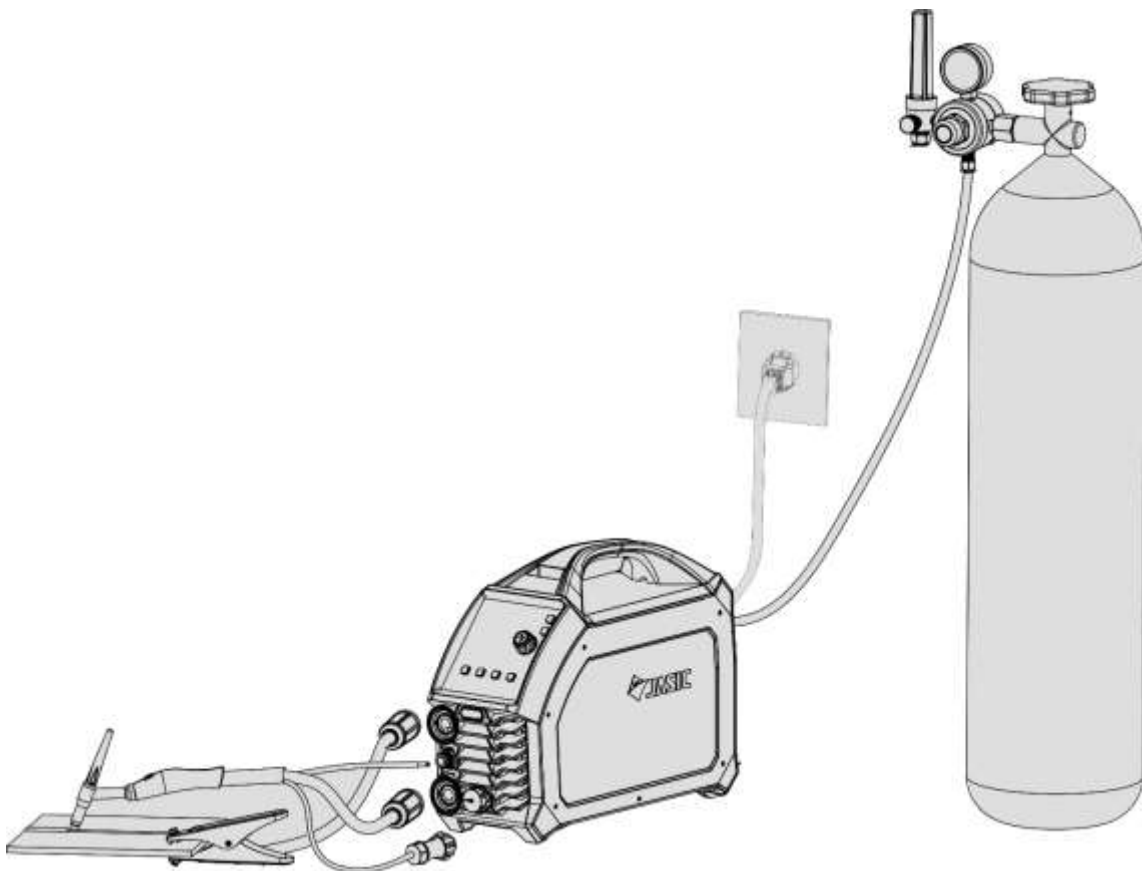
Anschluss von Schweißbrenner, Massekabel und Gasflasche
